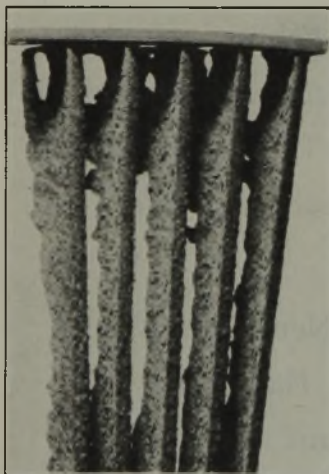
Durch Stillstandskorrosion weitgehend zerstörte Laufschaufeln einer Turbine.
